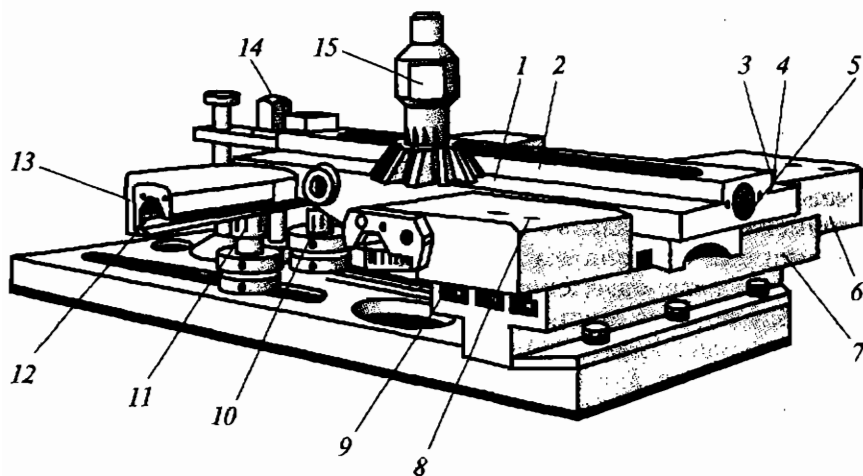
Приспособление для ремонта направляющих кареток суппортов с установленной кареткой:
